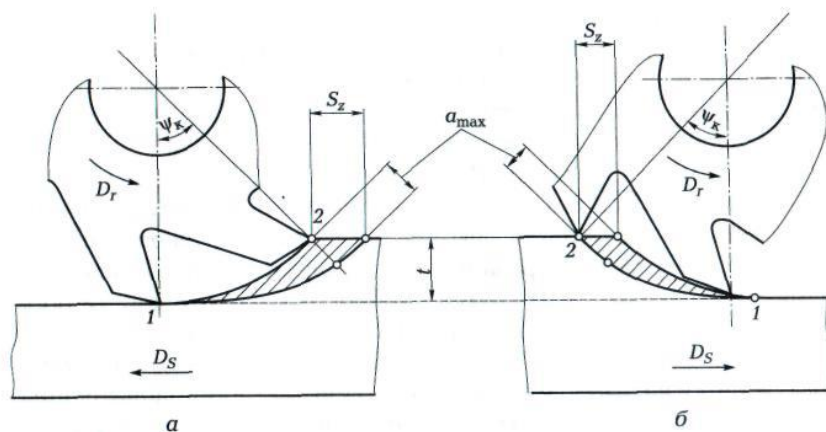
Схемы встречного (а) и попутного (б) фрезерования:
